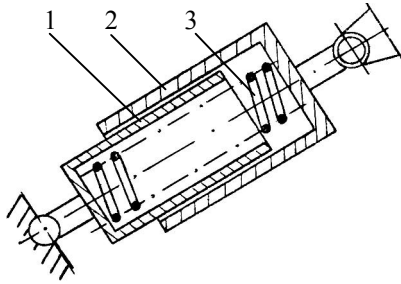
Пружинний зрівноважувальний механізм:
